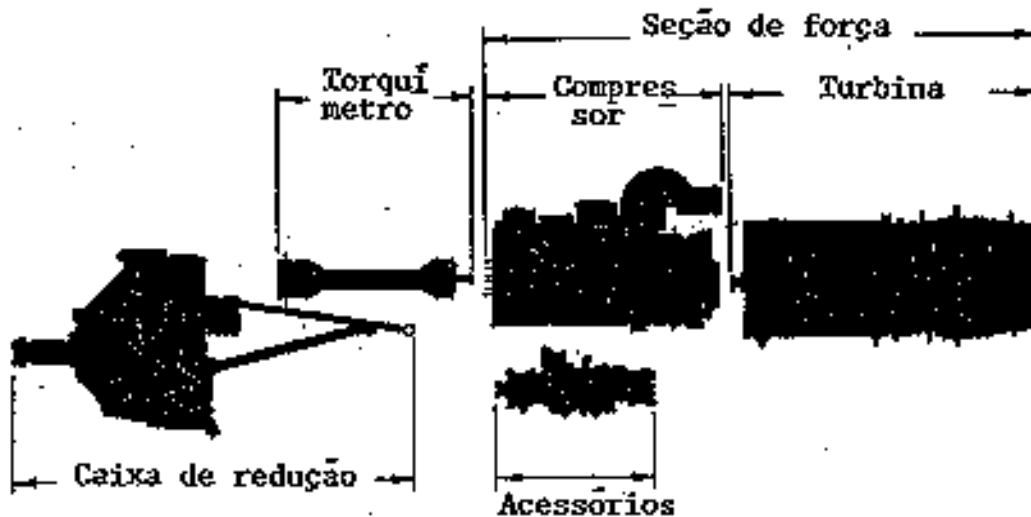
Conjuntos de componentes principais de um motor turboélice.
